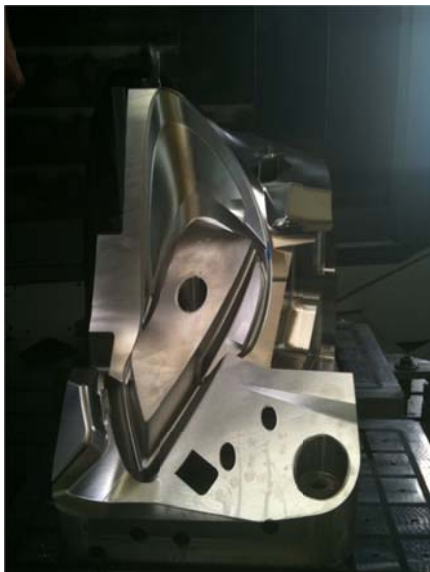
Imagem de um molde acabado de sair da máquina fresadora.
